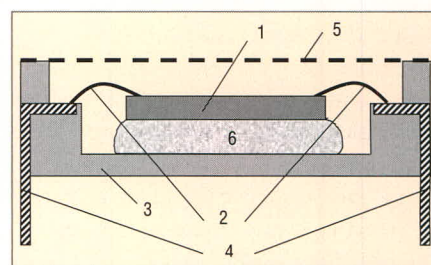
Схема размещения кристалла сенсора в корпусе (разрез, масштаб не соблюден): 1 – кристалл датчика; 2 – алюминиевые проводочные выводы; 3 – керамическое дно корпуса; 4 – металлические выводы корпуса; 5 – защитная сетка; 6 – теплоизолирующий слой
